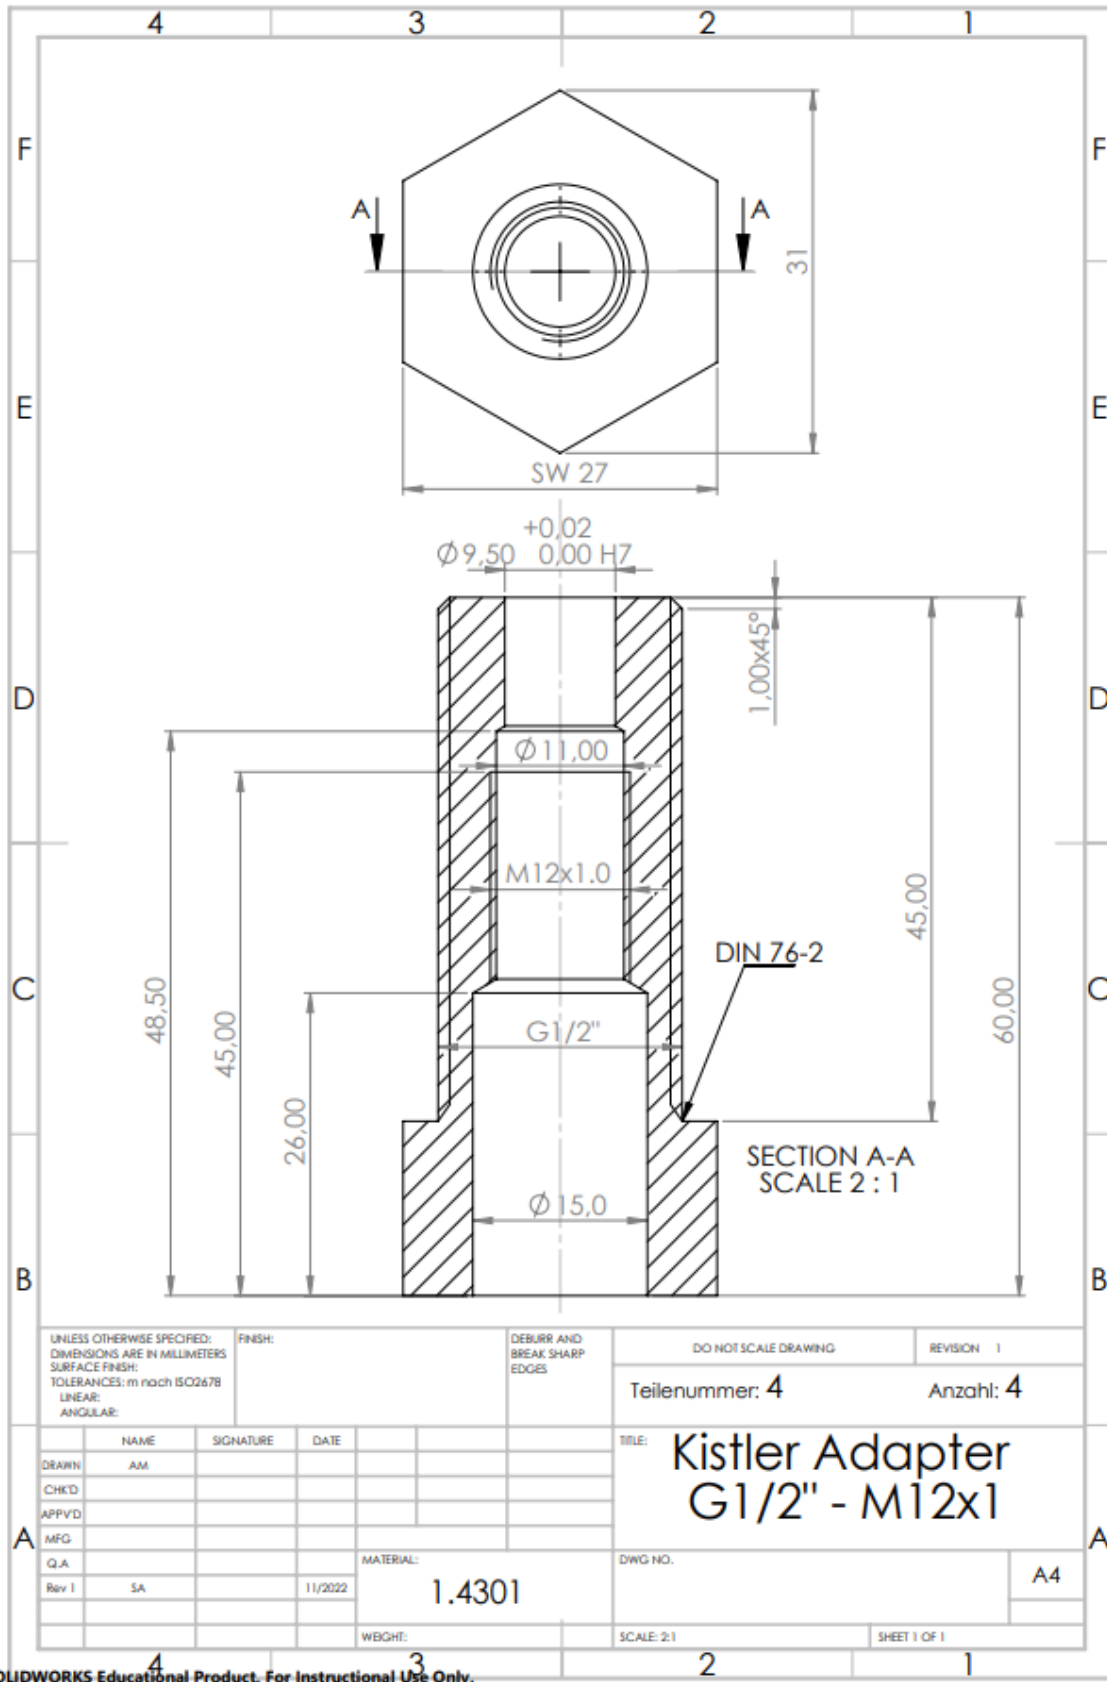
Technische Zeichnung des Kistler Adapters 1/2" - M12x1 (Teilenummer 4)
